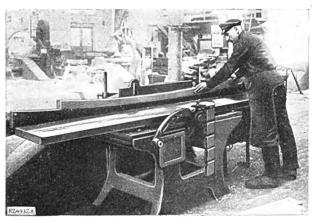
Abrichten des äußeren Bogens des Dachspriegels auf der Fräsmaschine
